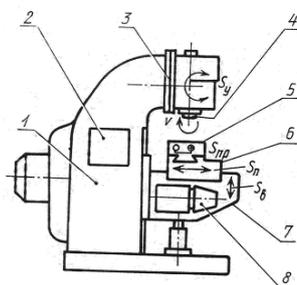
Вертикально-фрезерный станок: 1 – станина; 2 – коробка скорости; 3 – поворотная шпиндельная головка; 4 – шпиндель; 5 – стол; 6 – салазки; 7 – консоль; 8 – коробка подачи.
